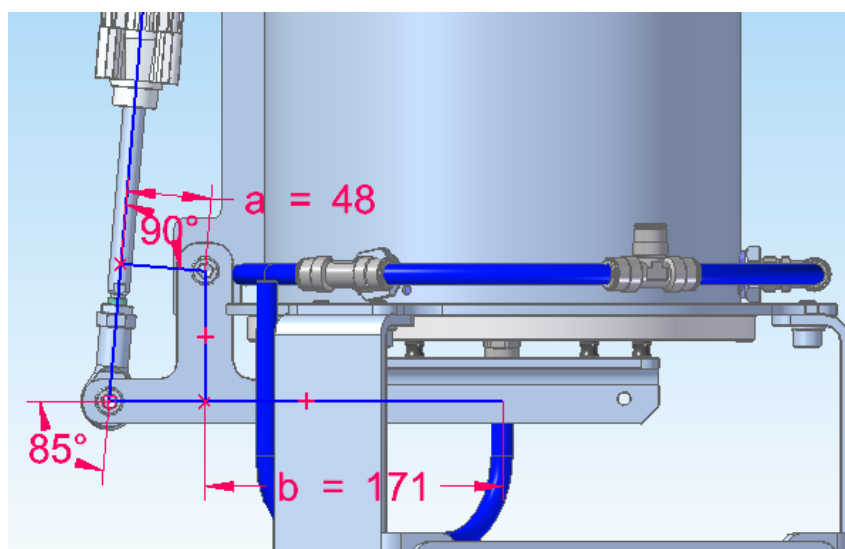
Geometrica di calcolo per dimensionamento impianto pneumatico
